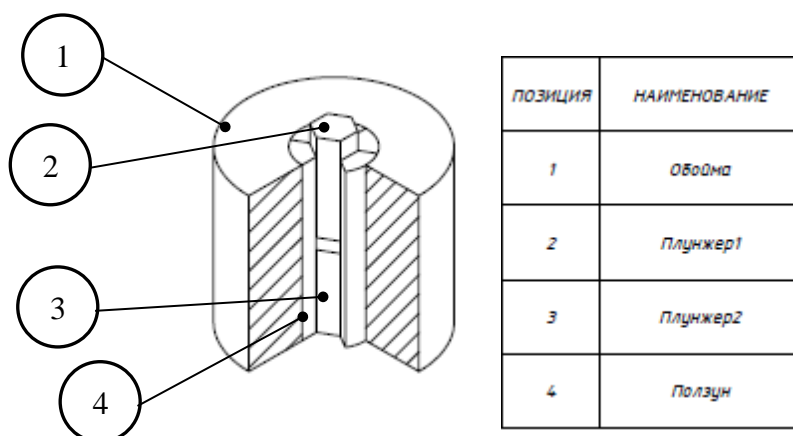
Конструкция коллекторной пресс-формы для изготовления изделий в форме шестигранной призмы
